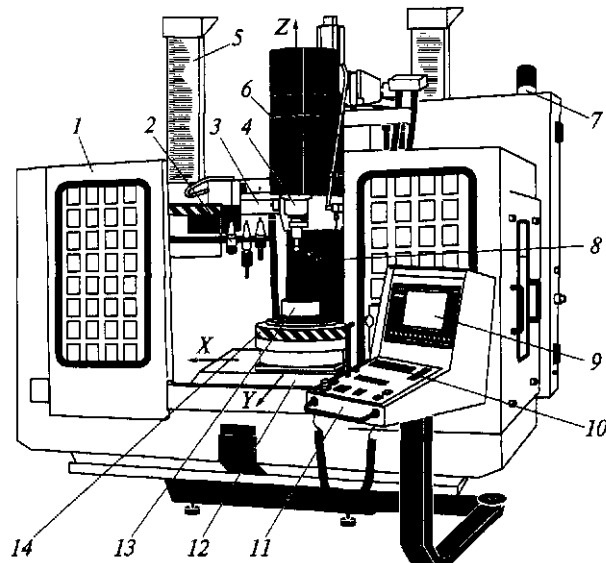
Зона обработки многоцелевого фрезерно-токарного станка: 1 — защитный кожух рабочей зоны; 2 — инструментальный магазин; 3 — направляющие инструментального магазина; 4 — шпиндель; 5 — телескопическое защитное устройство направляющих; 6 — шпиндельная бабка; 7 — лампочка световой сигнализации; 8 — сопла подачи СОЖ; 9 — дисплей; 10 — алфавитно-цифровая клавиатура; 11 — УЧПУ станка; 12 — салазки; 13 — заготовка; 14 — поворотный стол
